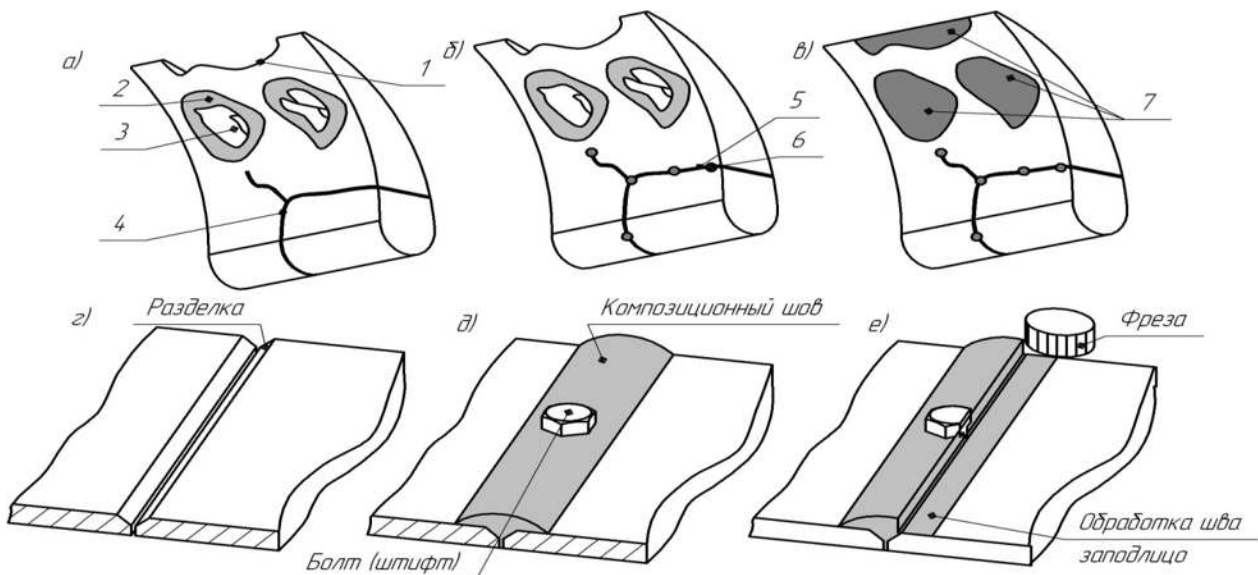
Ремонт дефектов лопасти рабочего колеса насоса: а – лопасть рабочего колеса с дефектами; б – ремонт трещины лопасти рабочего колеса; в – восстановление разрушенной кромки лопасти и заполнение раковин, свищей, сквозных отверстий НПК; г - разделка краев трещины; д – установка армирующих резьбовых элементов (штифтов, болтов) в подготовленные отверстия трещины; е – механическая обработка композита совместно с армирующими резьбовыми элементами; 1 – разрушение кромки лопасти; 2 – раковины и свищи; 3 – сквозные отверстия; 4 – трещина; 5 – композиционный материал в трещине; 6 – армирующий резьбовой элемент; 7 – композиционный материал в раковинах, свищах, сквозных отверстиях.
